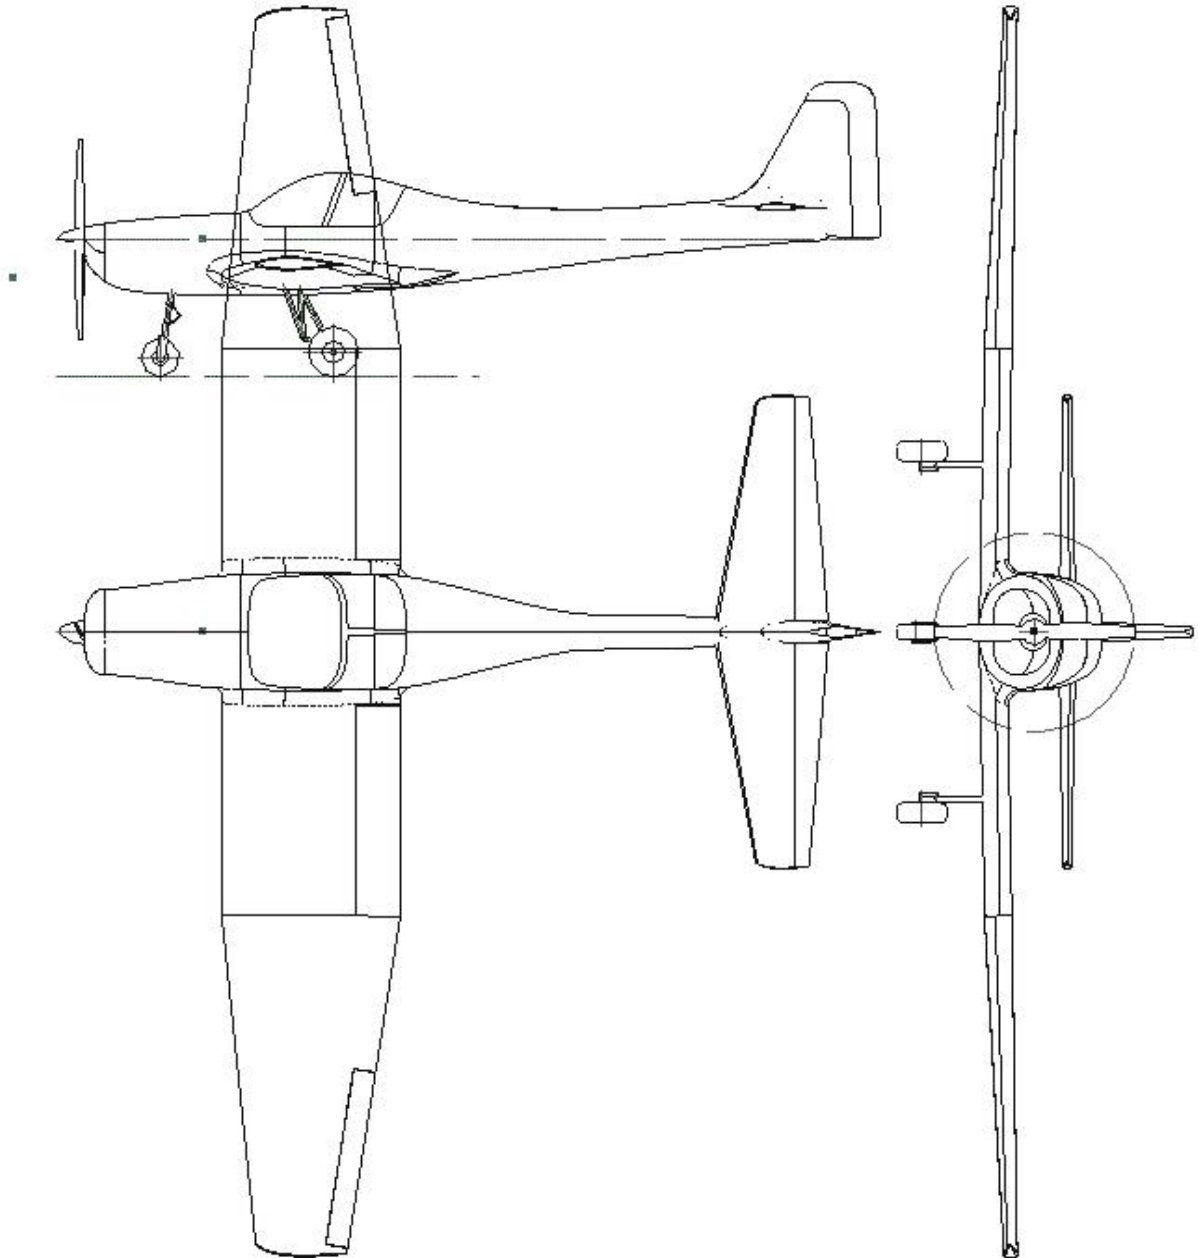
Primeiro avião em CAD 3D – Asa reto-trapezoidal
